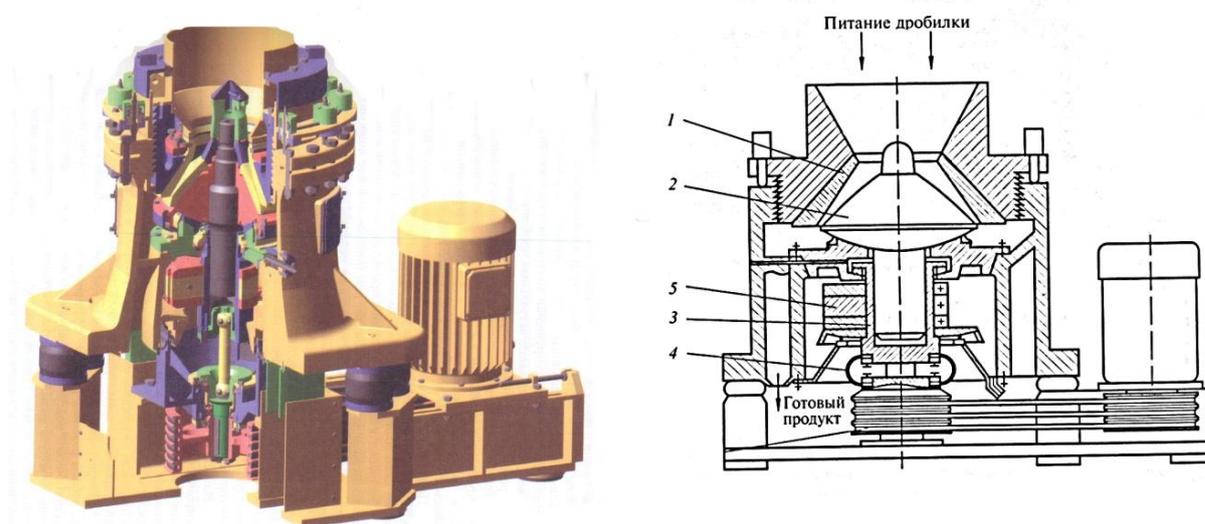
Принципиальная схема и общий вид промышленной дробилки КИД: 1 – цилиндрическая чаша; 2 – дробящий конус; 3 – вал; 4 – гибкая трансмиссия; 5 – дебалансный вибратор
